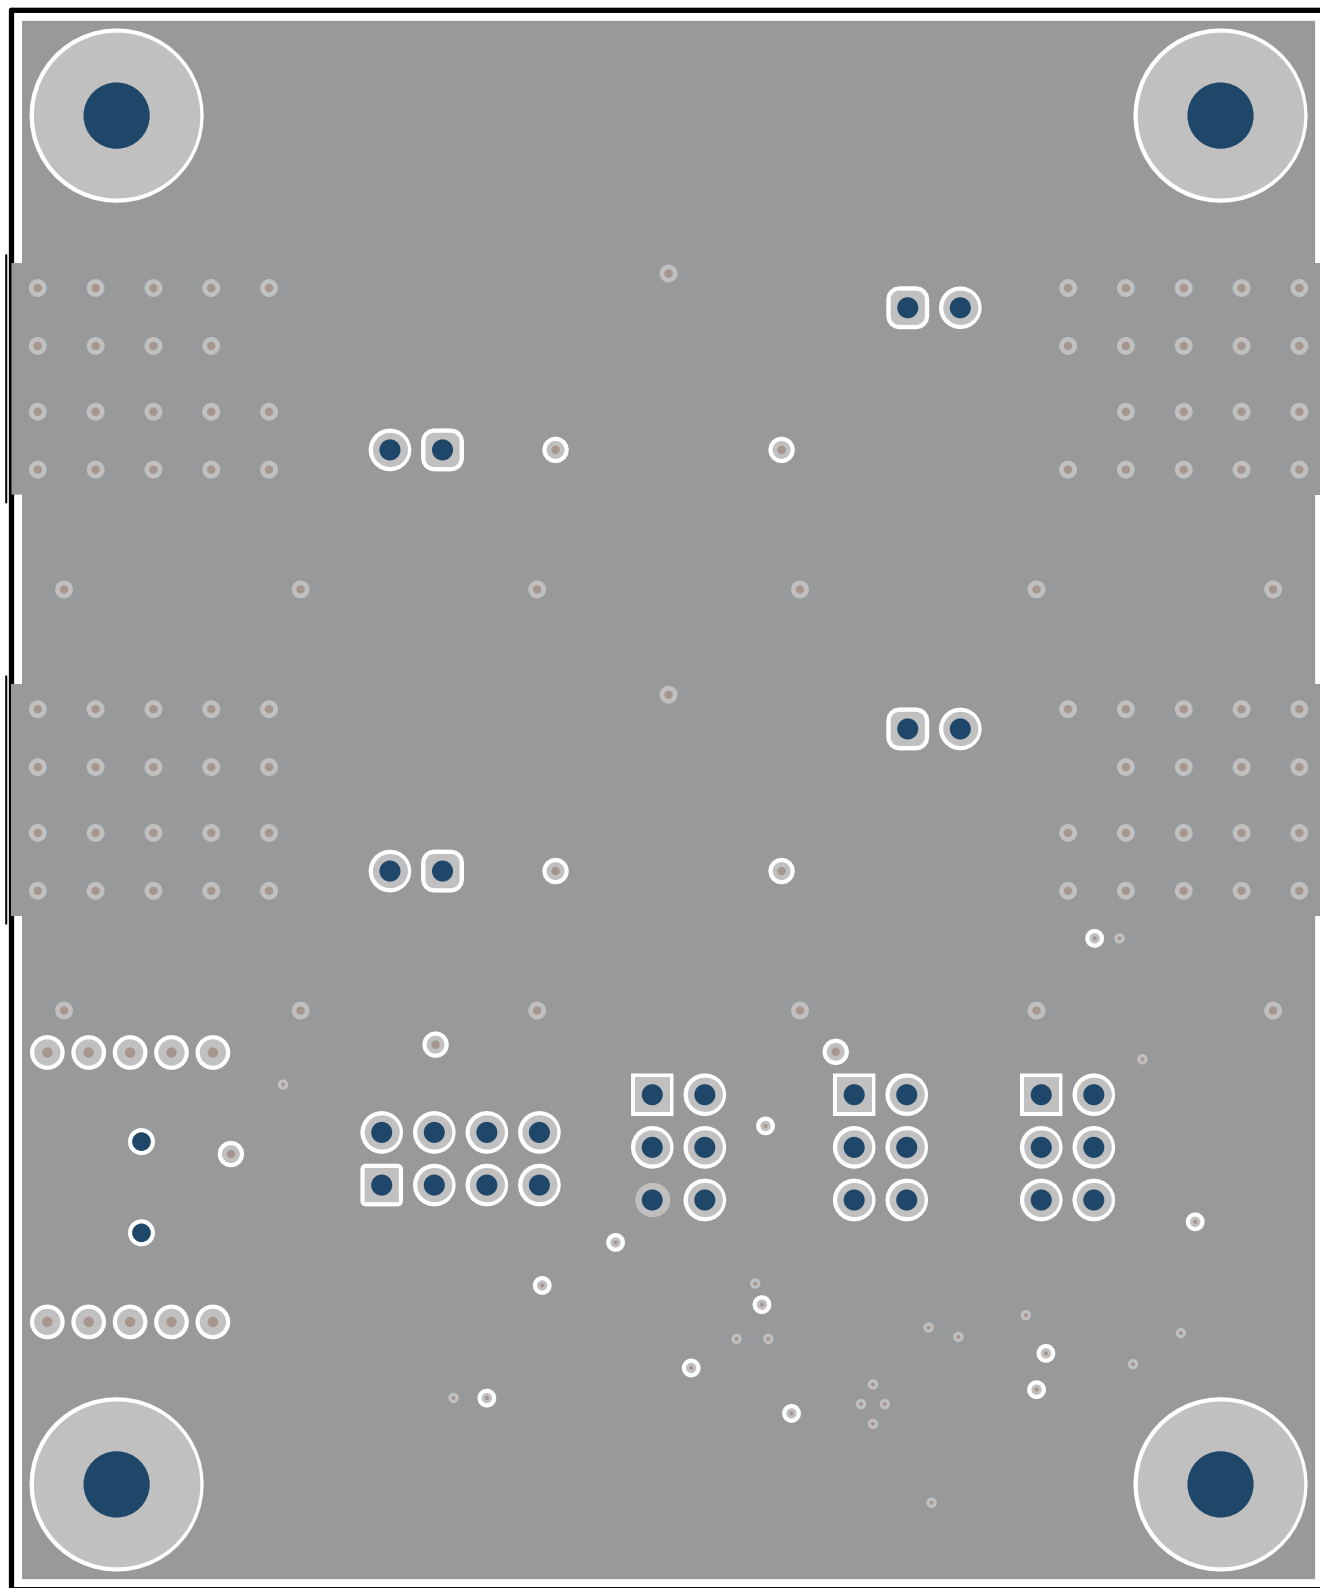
CDC6 EVM の PCB レイアウト例 — GND レイヤ
